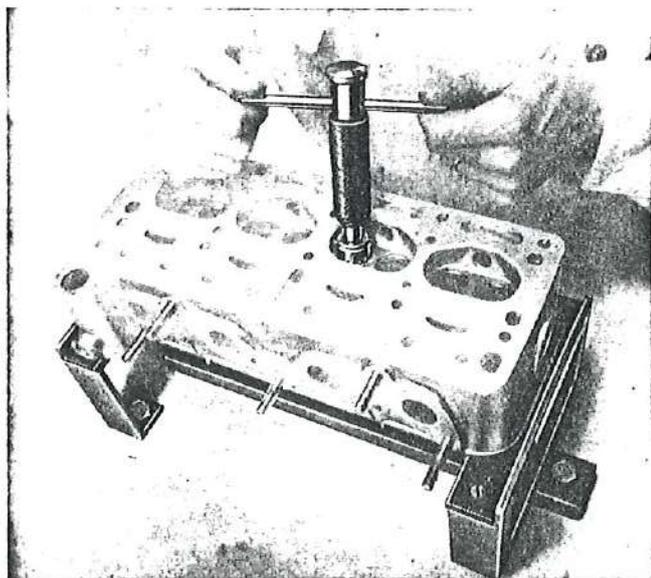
Reducción de la anchura de asientos de válvulas con la fresa A.11457 (de 75°) y el mandril A.11482. La fresa de 75° quita material en la parte baja del asiento.
